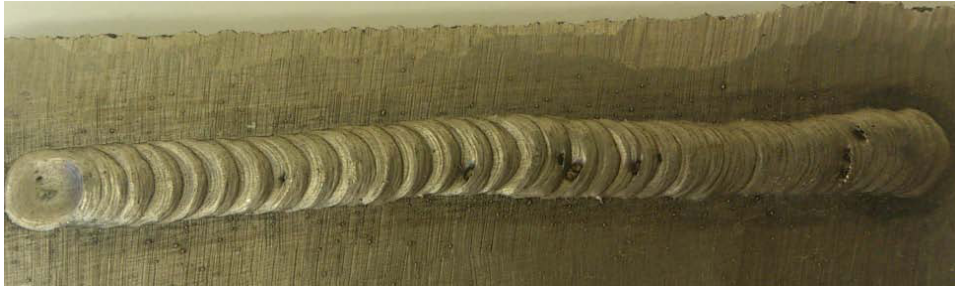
Пористость в металле, наплавленном сварочной проволокой НП1 на сталь 04Х20Н6Г11М2АФБ
